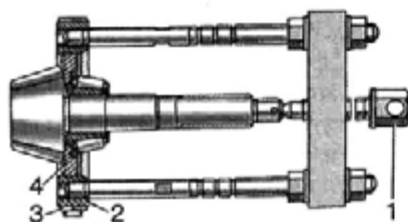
Снятие подшипника с ведущей шестерни главной передачи:
